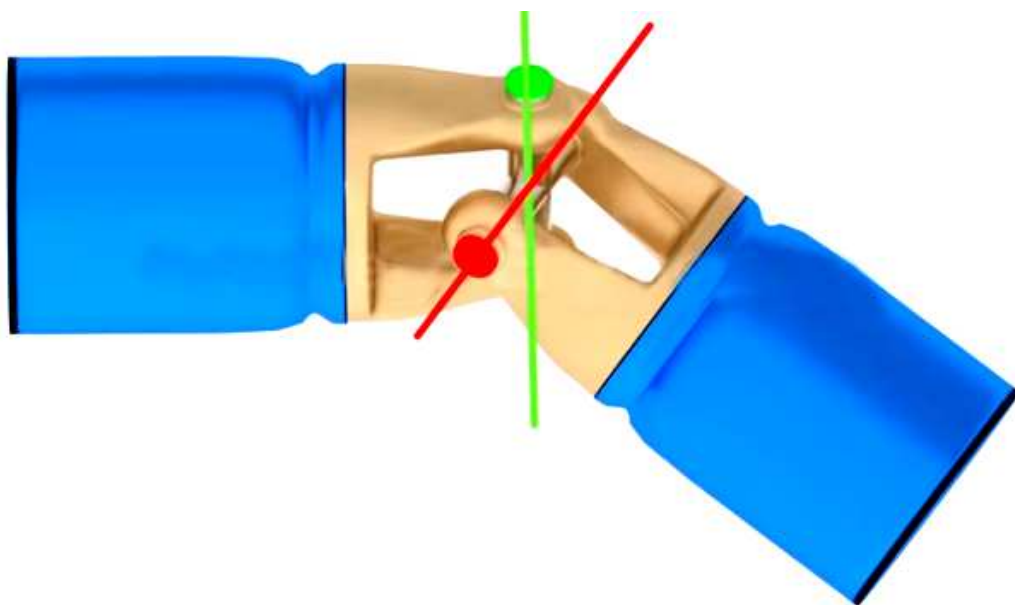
Универсальный шарнир модель – схема – движение под углом
